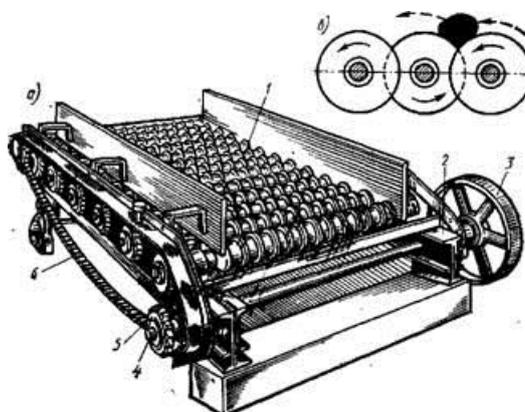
Валковый грохот общий вид (а): 1 –валок; 2- наклонная рама; 3 – привод; 4 – главный вал; 5 – приводная звездочки; 6 –цепная передача и схема движения материала (б)
